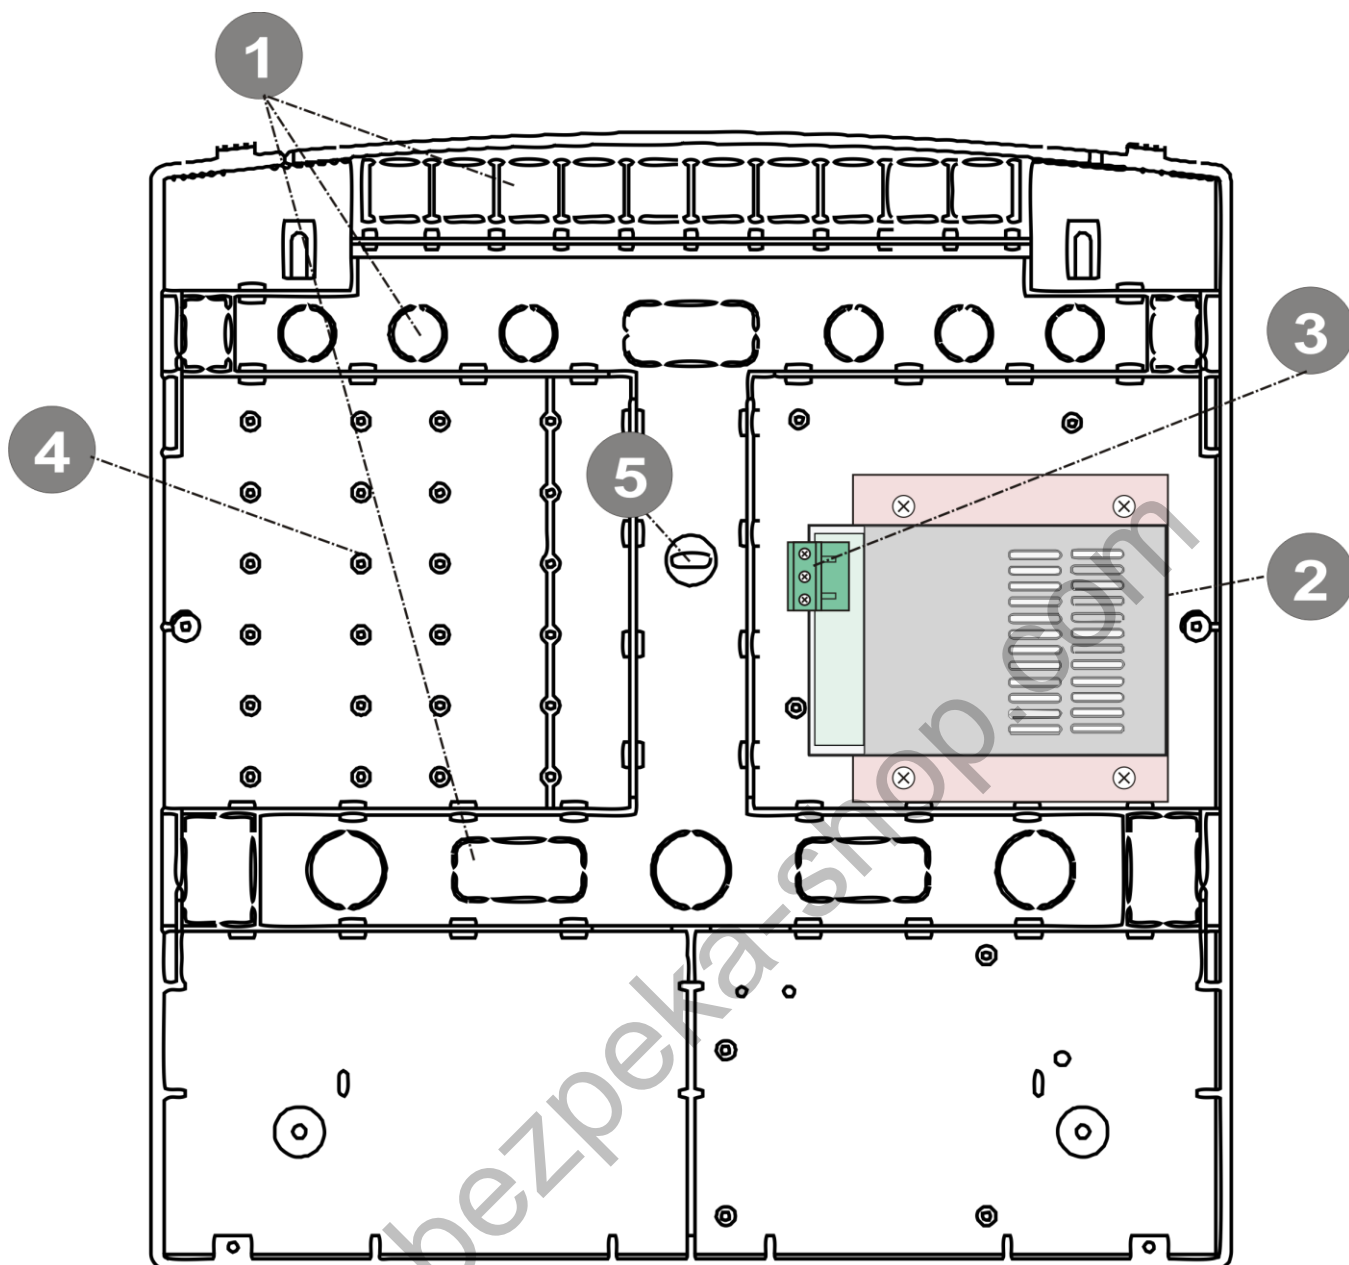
Внешний вид корпуса ППКП без основного модуля:
